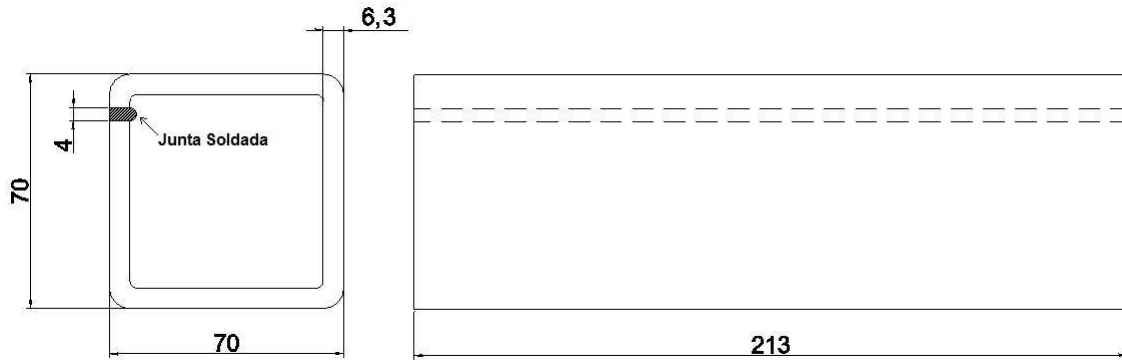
Dimensões da amostra (cotas em mm) e a localização da junta soldada (costura).
